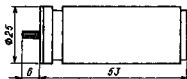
28 Габаритные и установочные размеры двигатель-генератора АДГ-004
